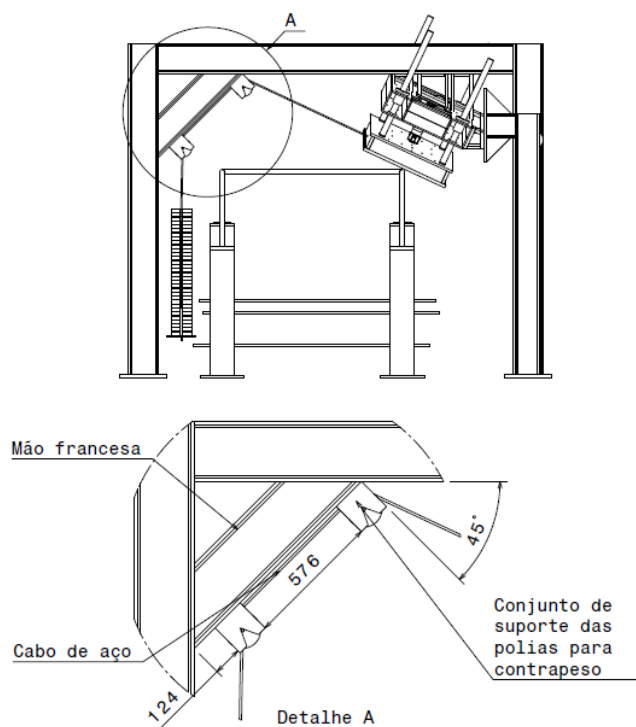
Vista posterior do dispositivo RoofCrush (+ Cage) com foco no sistema de contrapesos tangencial. (Fonte: autoria própria)
